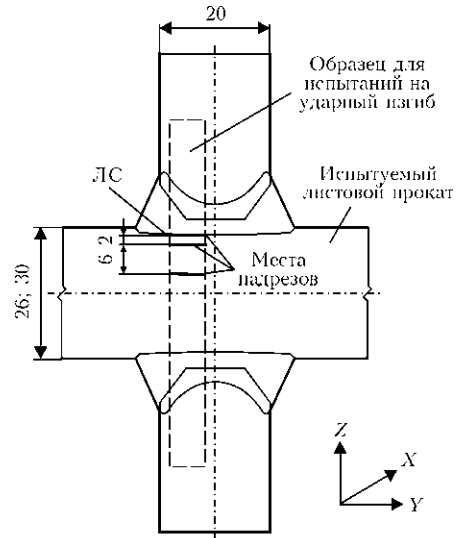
Схема вырезки образцов из крестообразных сварных соединений с указанием мест нанесения надреза
